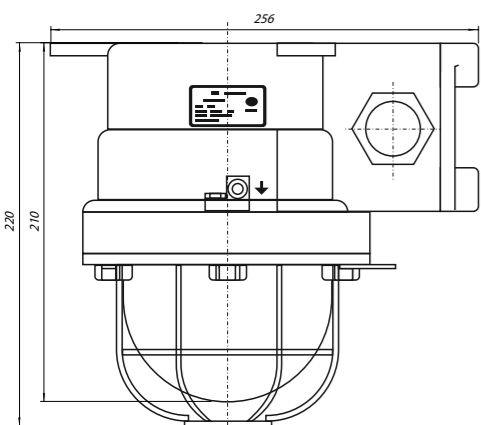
Светильник со сгонами под прокладку кабеля в трубах
